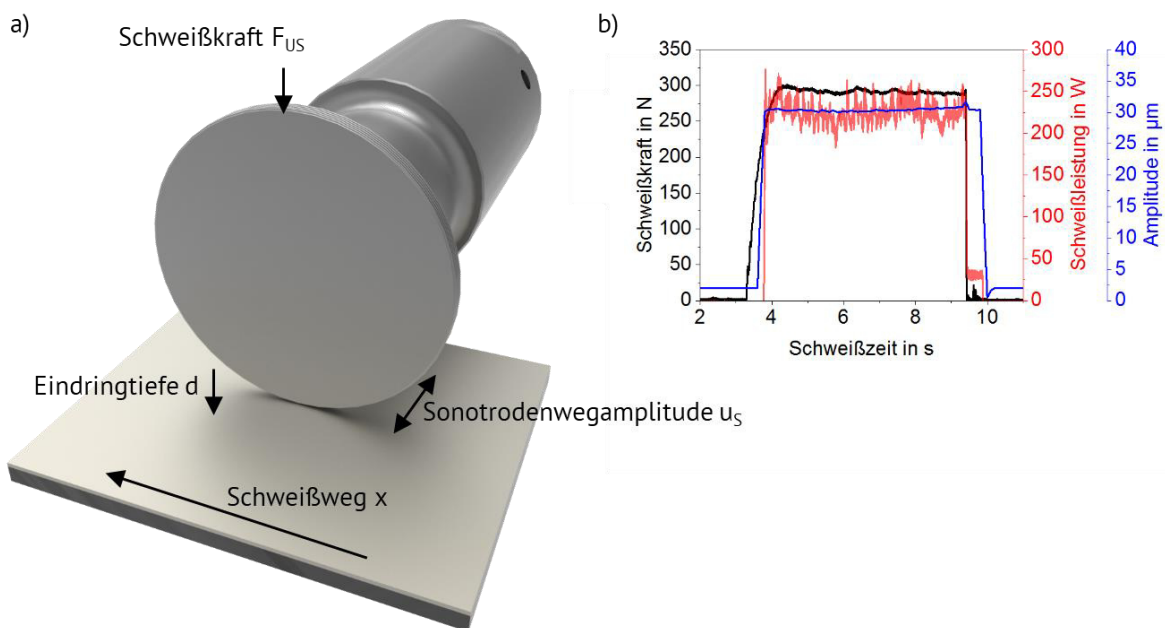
a) Betrachtete Prozessparameter der Translationsschweißanlage und b) exemplarischer Messwertverlauf der wichtigsten Prozessgrößen einer 80 mm Schweißnaht ( $v = 12$  mm/s)
